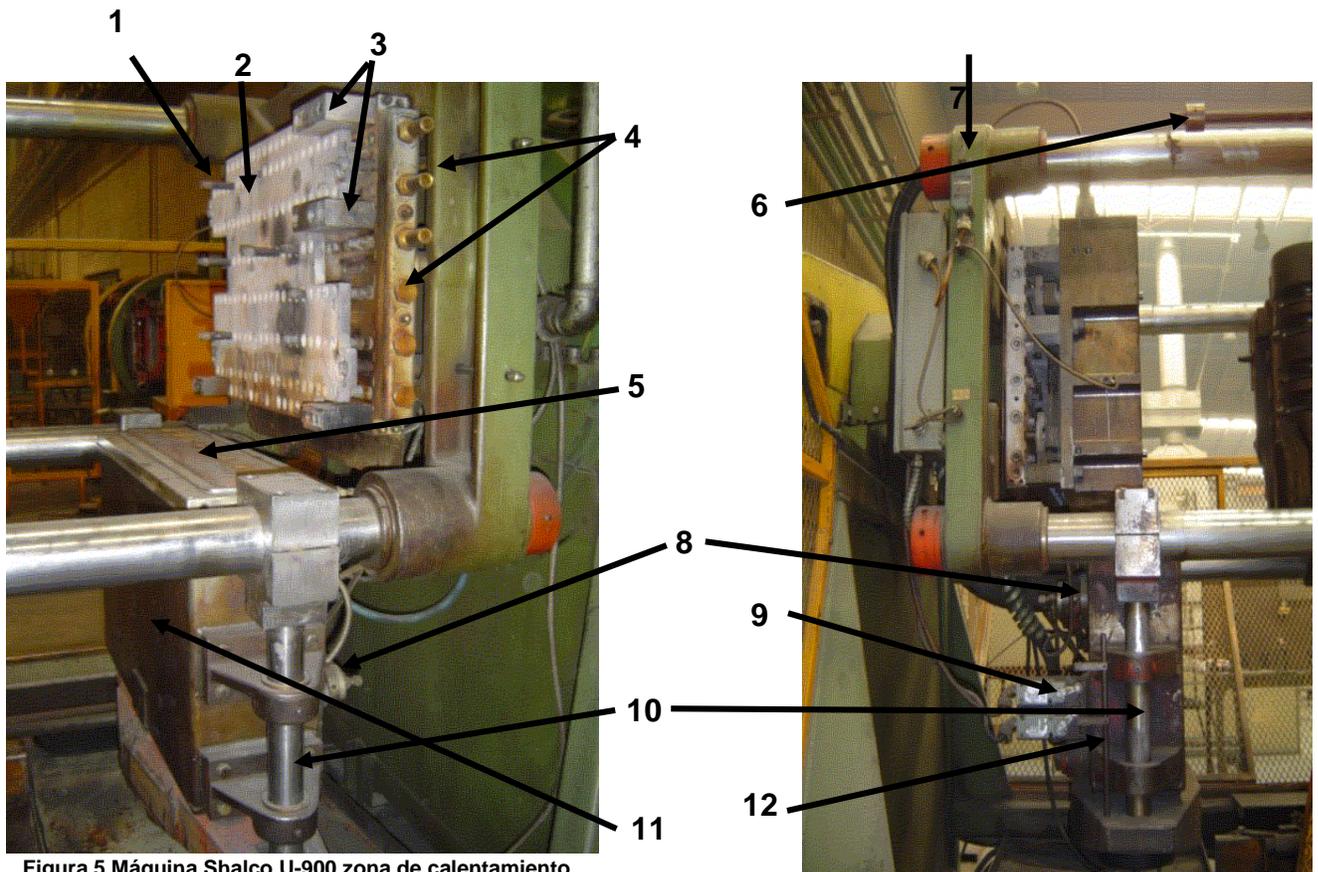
Máquina Shalco U-900 zona de calentamiento.
